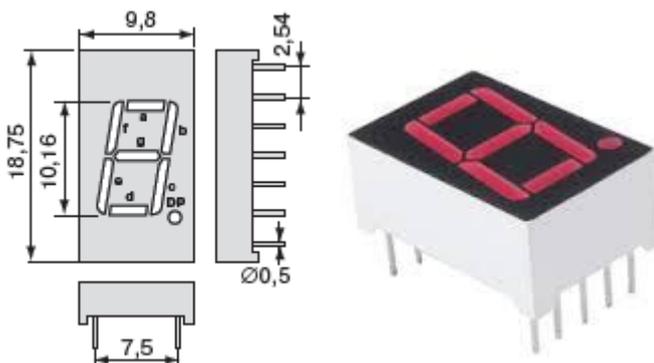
Размеры и внешний вид семисегментного индикатора и два марки DA56-11SRWA
